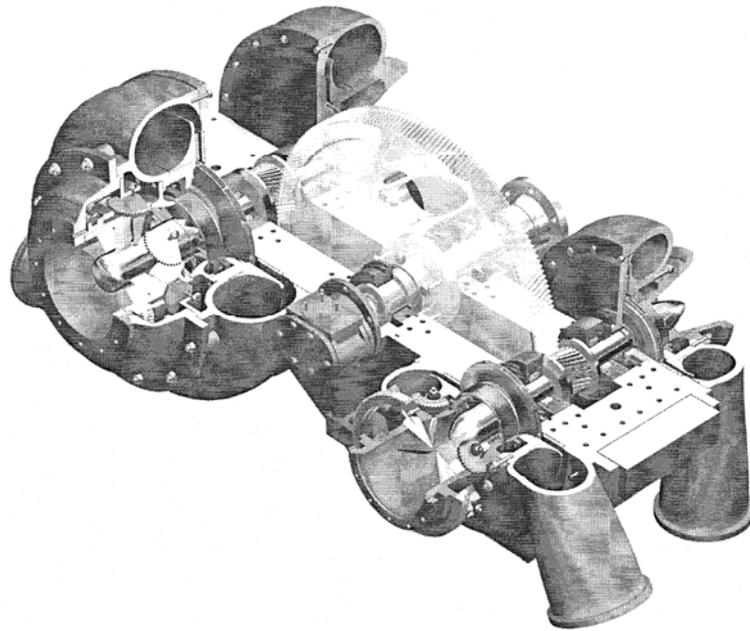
а. Двухвальный четырехступенчатый центробежный компрессор ОАО «Дальэнергомаш» для подачи воздуха в пневматические системы (корпуса ступеней и верхняя крышка корпуса повышающей зубчатой передачи сняты)
